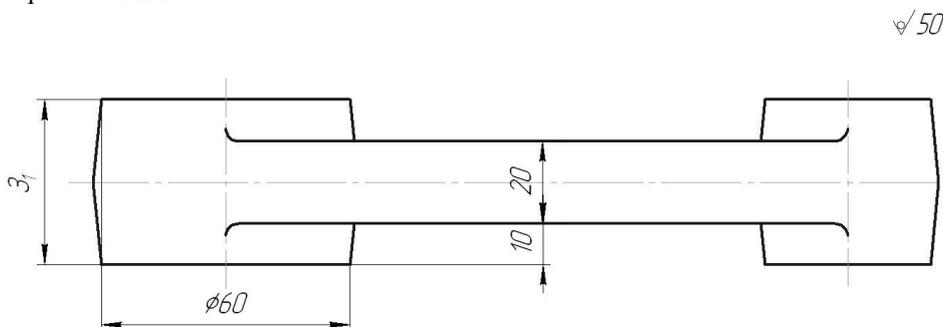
Чертеж заготовки (фронтальная проекция)
